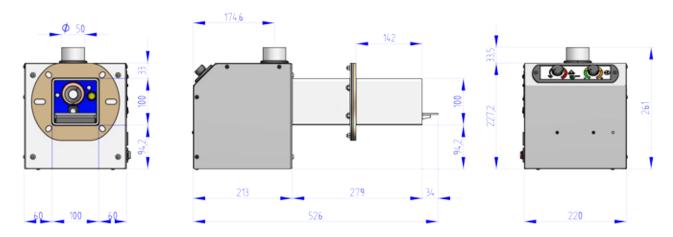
<sup>2</sup>. Dimensiones del quemador 'B-Home' (<sup>2</sup>cámara de combustión cuadrada)
